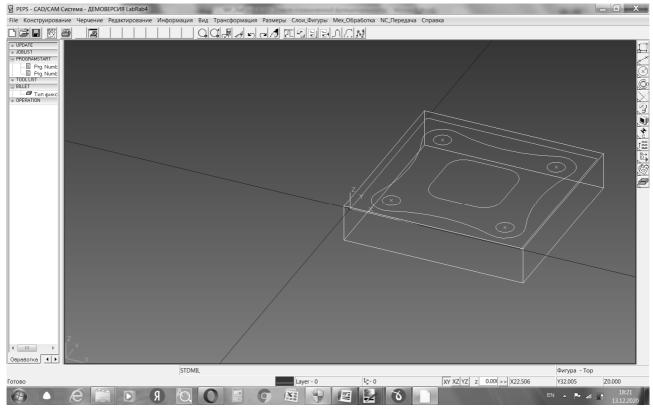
Вид заготовки и обрабатываемых контуров
